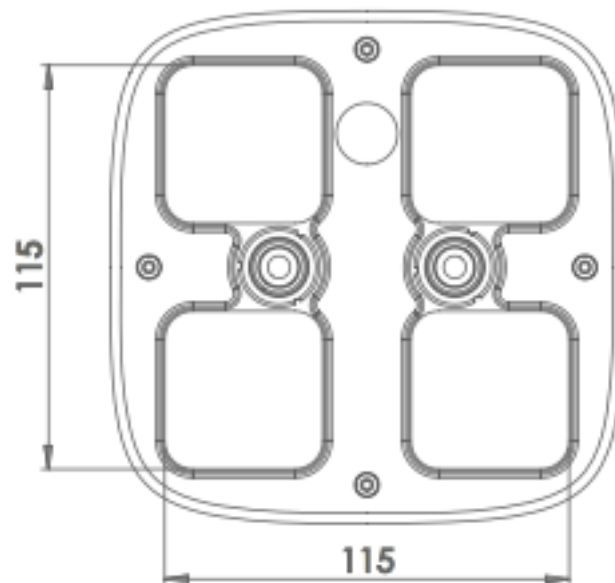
Dimensões da superfície de preensão (parte inferior) do Gecko Gripper.
